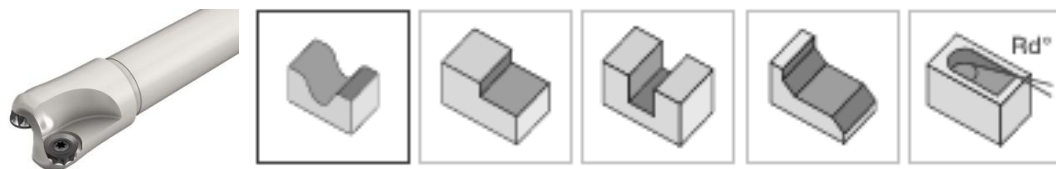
Загальний вигляд і оброблювальні поверхні кінцевих фрез типу ChamMill [5]
